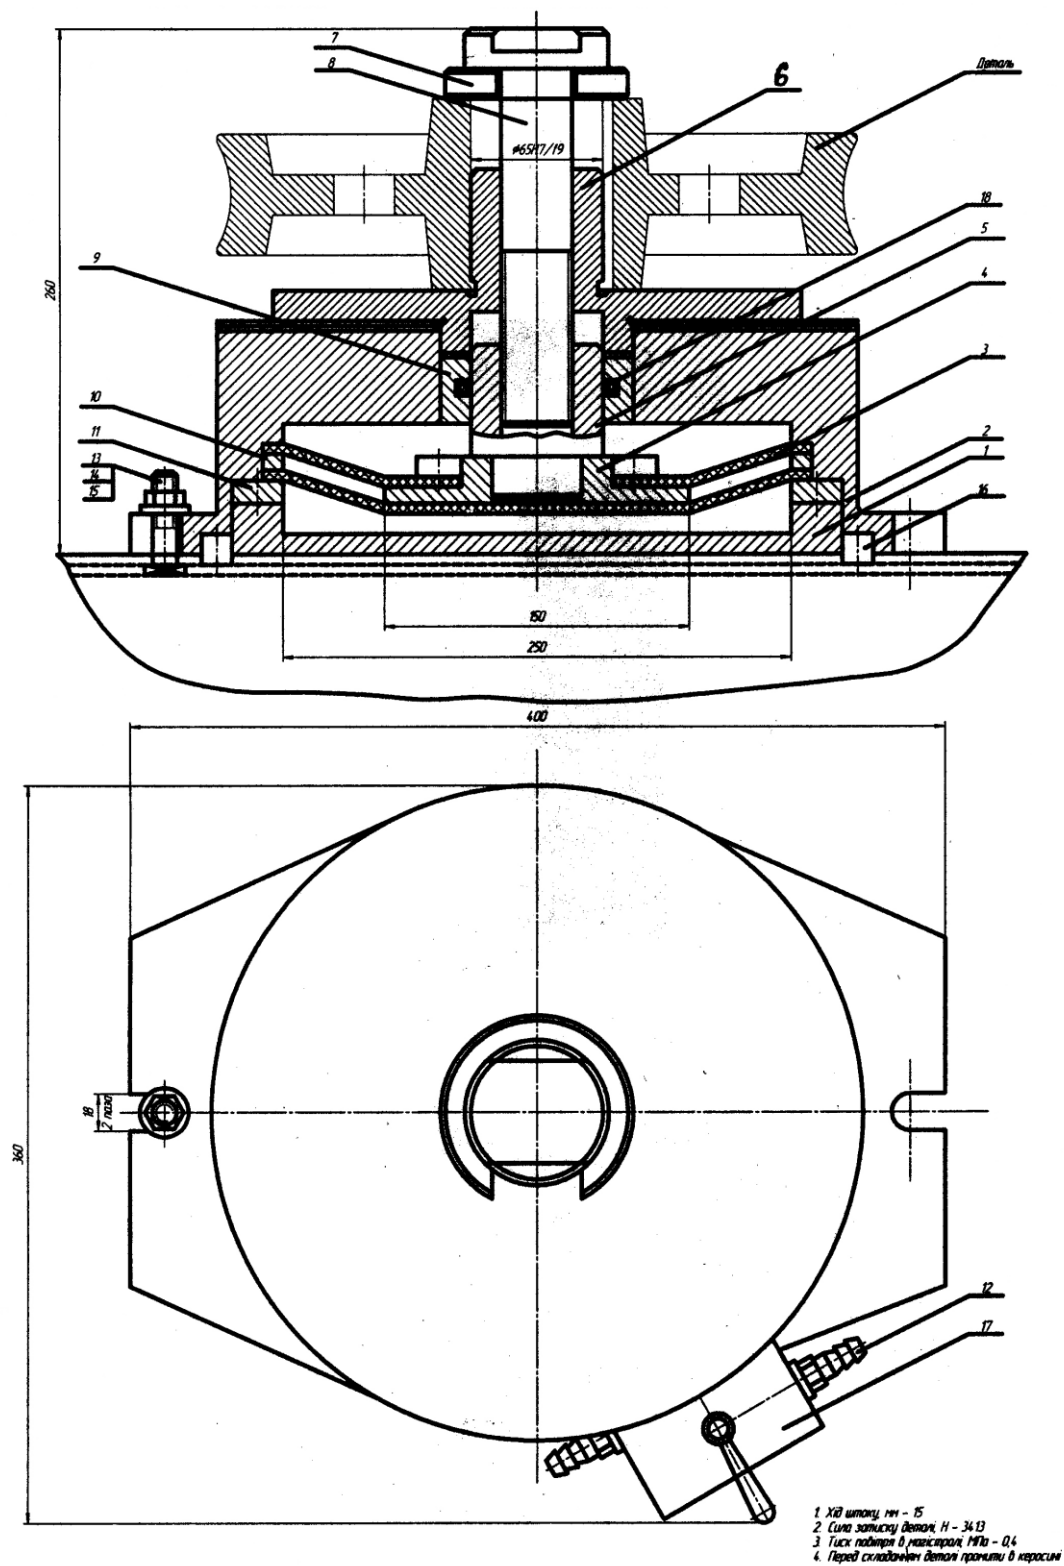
Пристосування для фрезерування зубців на зубофрезерному верстаті мод.5К324
